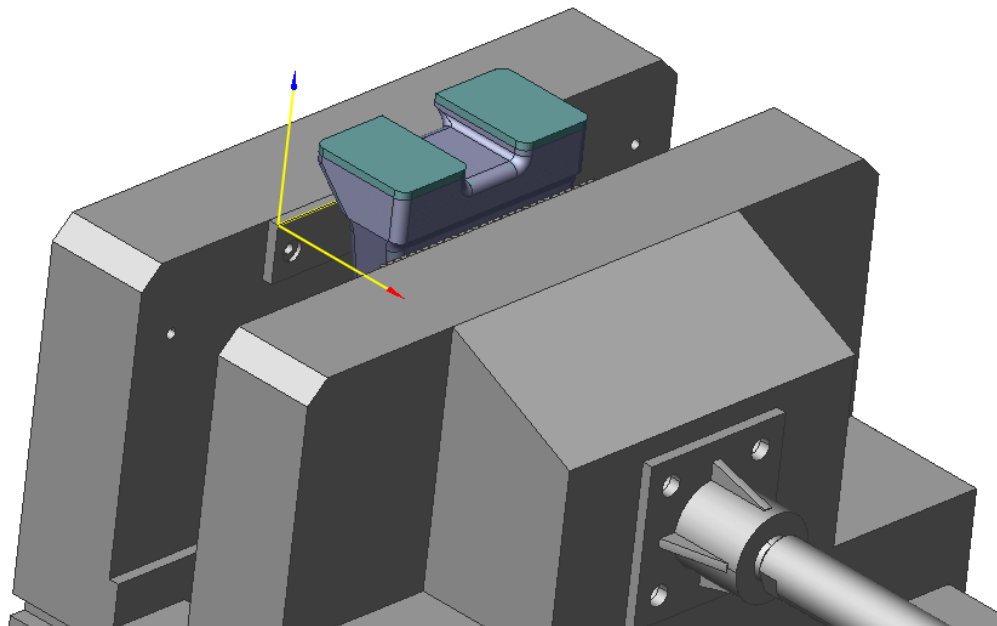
Базування та нульова точка координат заготовки при Базуванні 1
